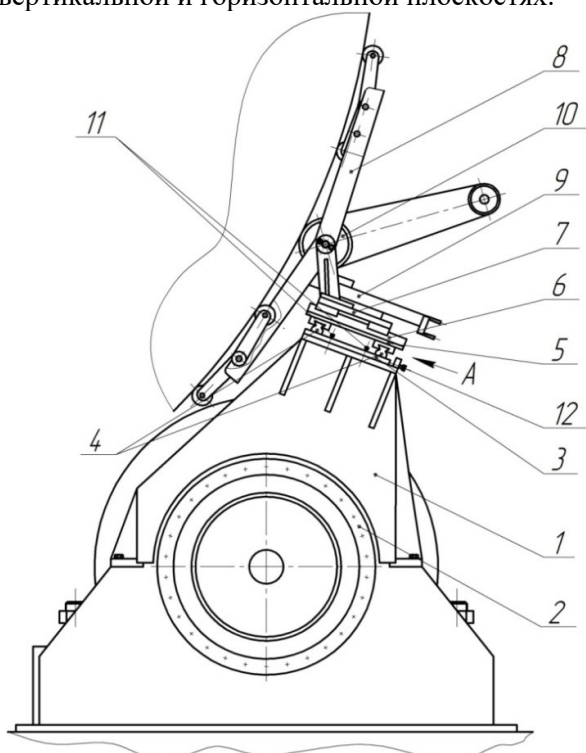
Облегченная конструкция ленточно-шлифовального станка
